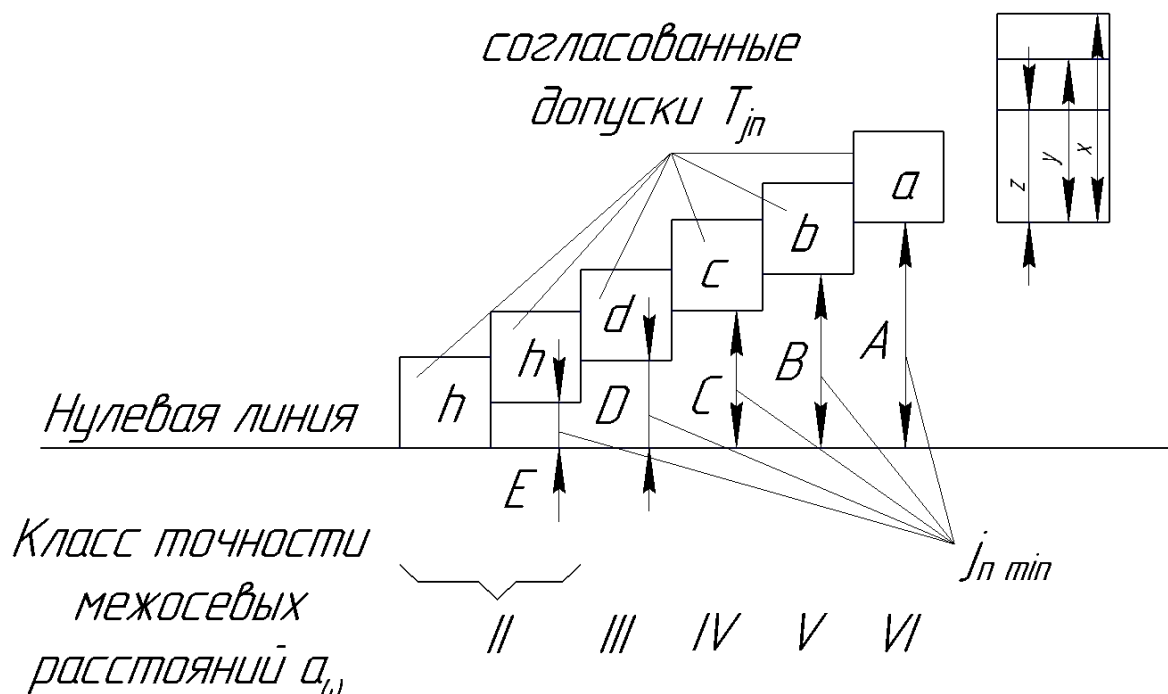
Схема расположения полей допусков T_{jn} для принятых видов сопряжений зубьев зубчатых колес
